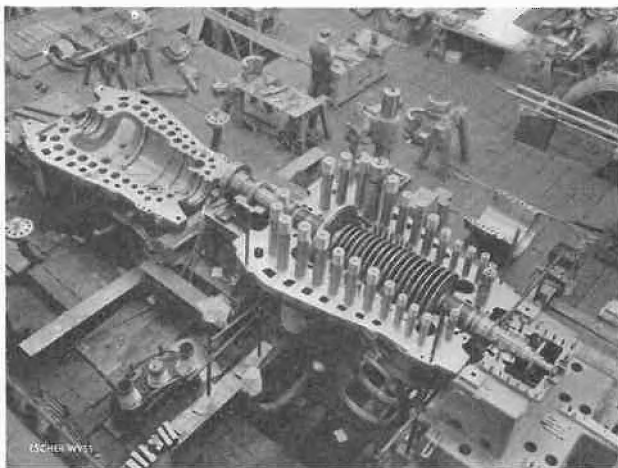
HD-Gehäuse für 170 at 600° einer 115 000-kW-Dampfturbine. Breite Teilflanschen mit Heizkanälen im äußeren Teil
